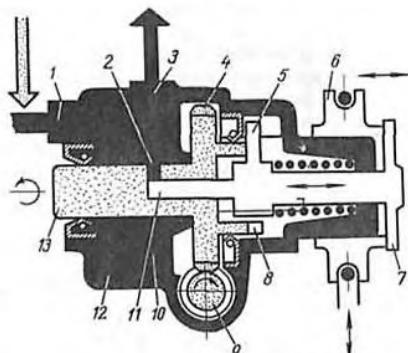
Схематический разрез насоса: 1 — подача масла; 2 — пункт дозирования смазки; 3 — выход масла; 4 — червячная шестерня; 5 — плунжер; 6 — регулировочный шкив; 7 — регулировочный диск; 8 — цилиндрический кулачок; 9 — червяк; 10 — впуск масла; 11 — плунжер; 12 — масляный резервуар; 13 — распределитель.
